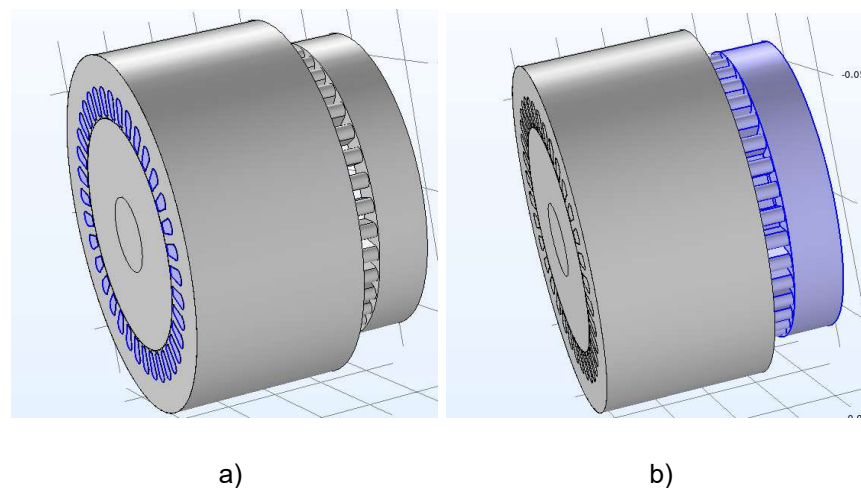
Desenho motor 3D. a) Destaque condutores parte ativa do núcleo b) Destaque condutores na cabeça de bobina.
